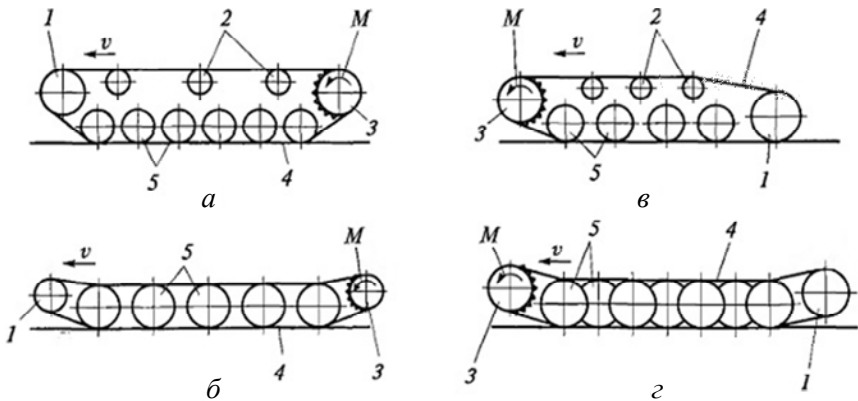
Схемы гусеничных движителей с кормовым (а, б) и носовым (в, г) расположением ведущего колеса:
